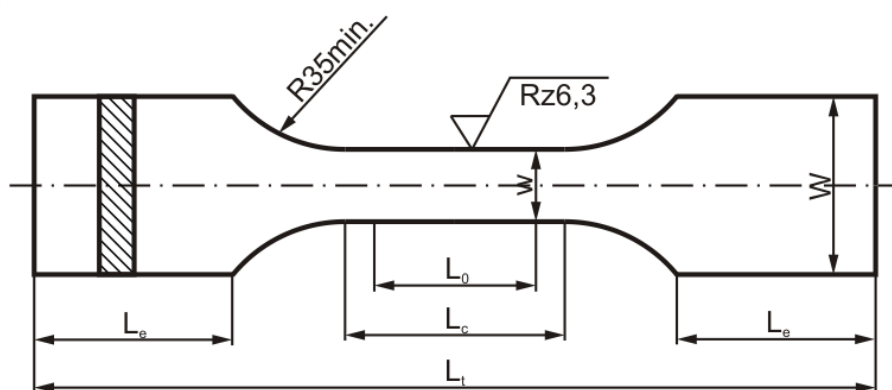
Flachzugprobe nach Form E DIN 50125 [49]
